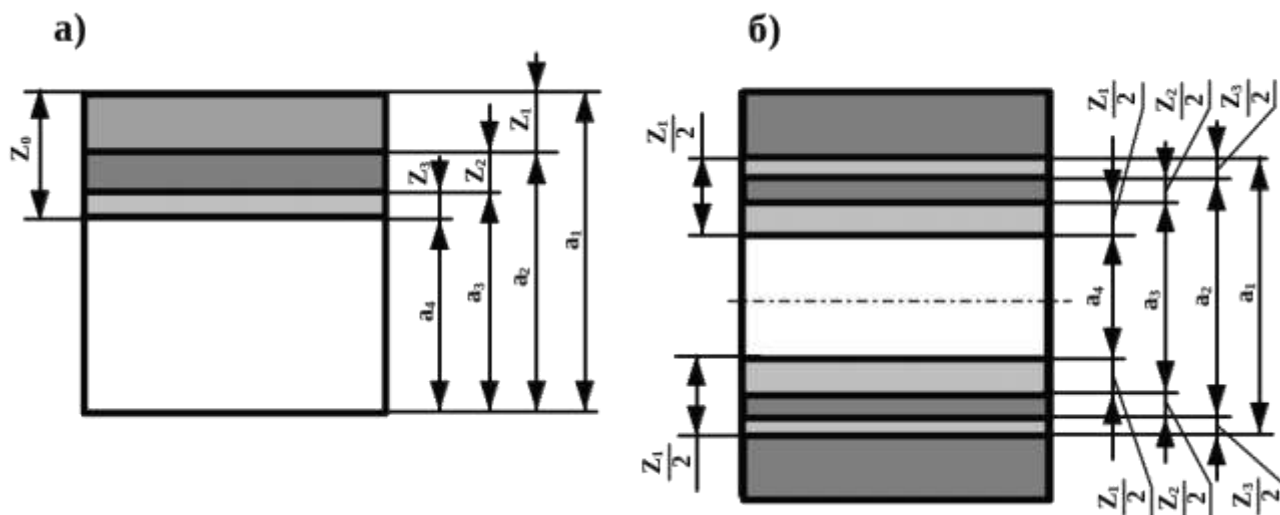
Припуск на обробку зовнішніх і внутрішніх поверхонь
